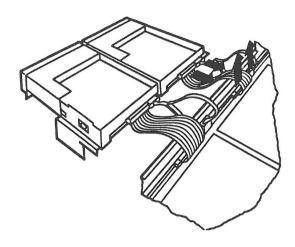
Kabel vom Diskettenlaufwerk entfernen
